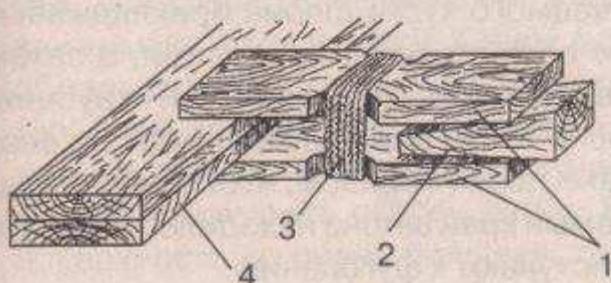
Приспособление для сжатия деталей: 1 — зажимные бруски; 2 — клин; 3 — металлические хомуты; 4 — детали
